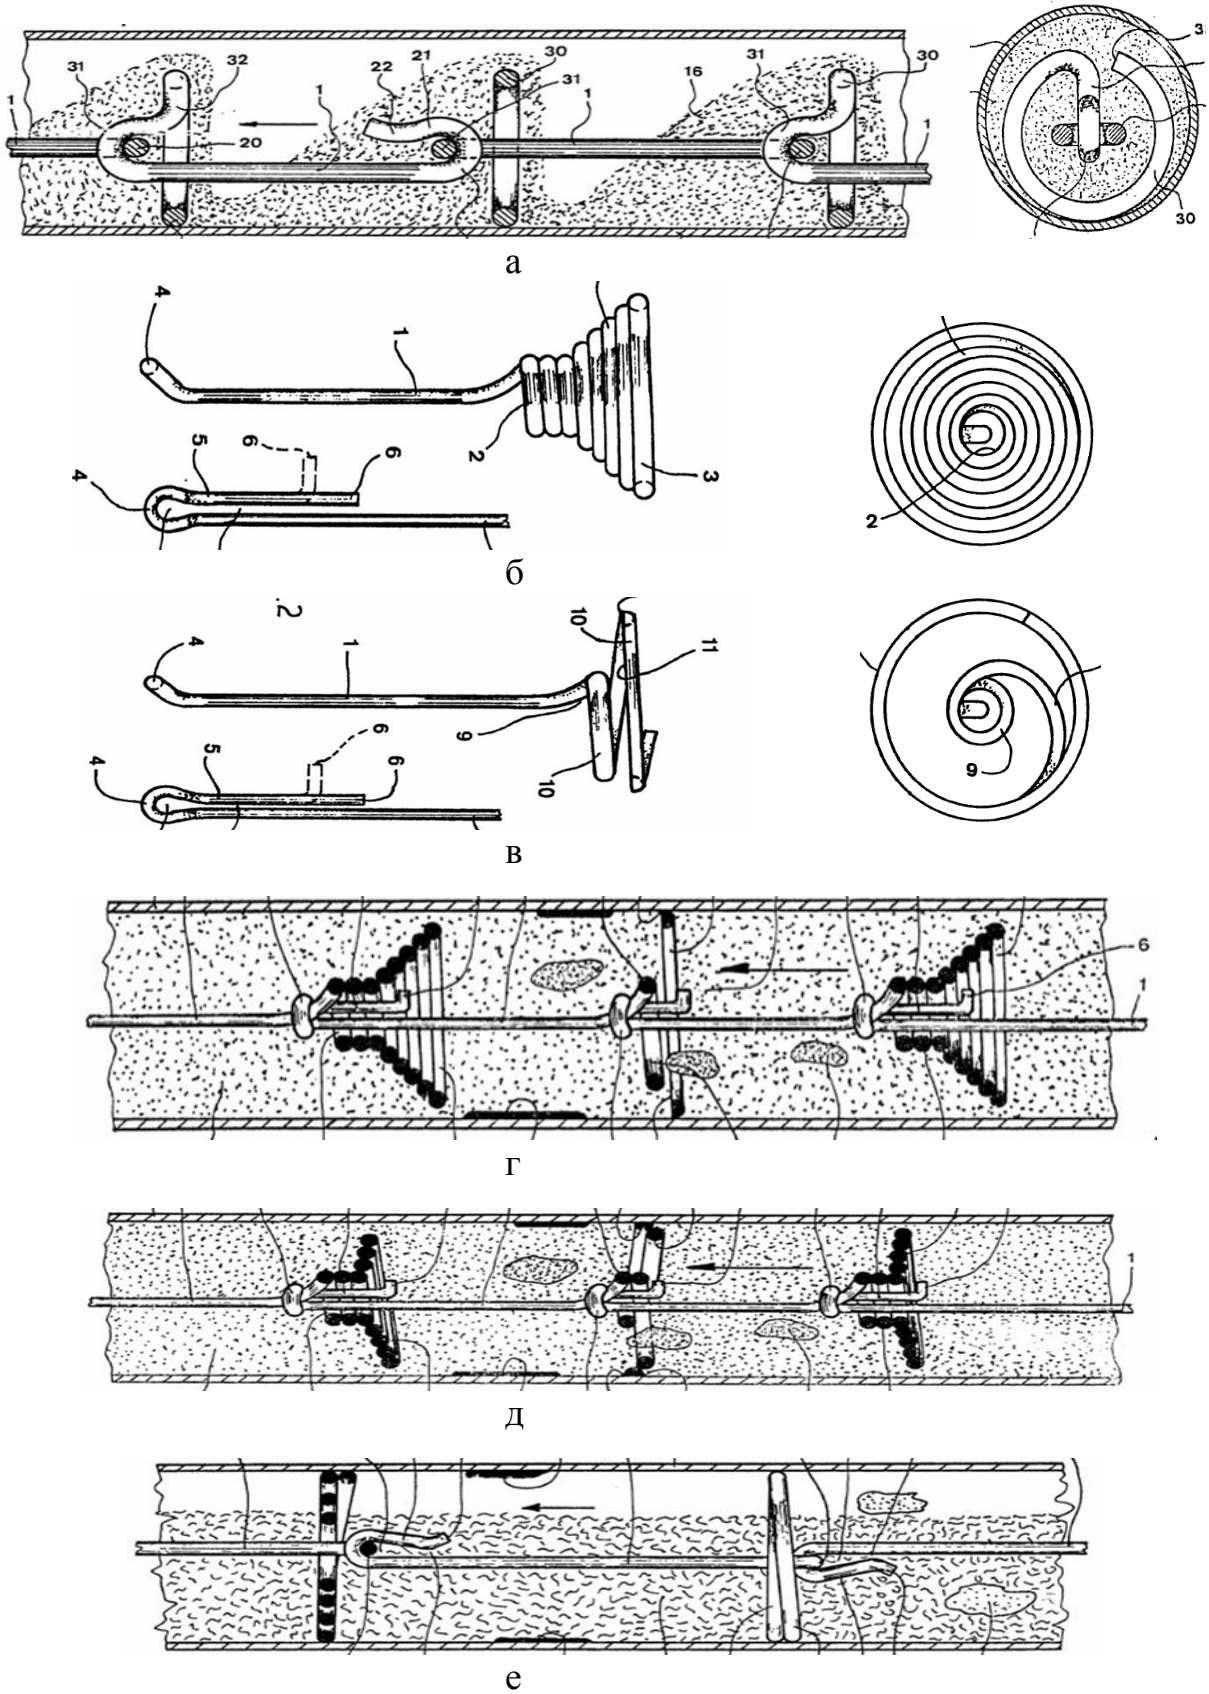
Пружинні робочі органи трубчатого конвеєра
